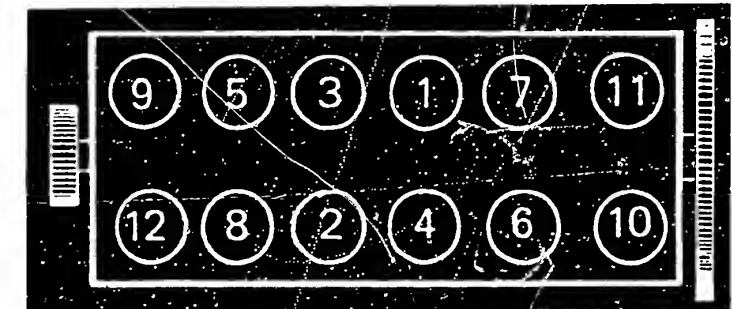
Die Zylinderkopfschrauben werden in dieser Reihenfolge in drei Schritten mit 40/60Nm und einem Drehwinkel von 180° angezogen.
